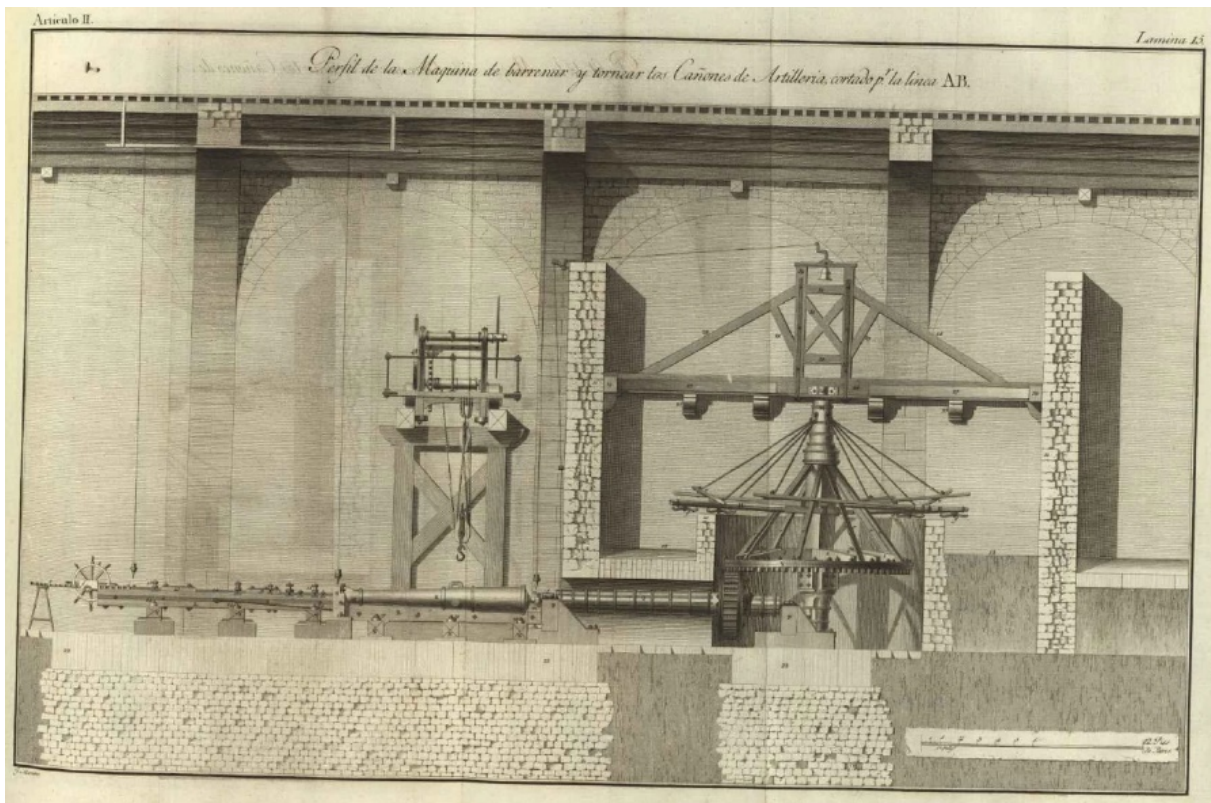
Plano de perfil de la máquina para barrenar y torner las piezas de artillería con su cabriolé correspondiente [3].
